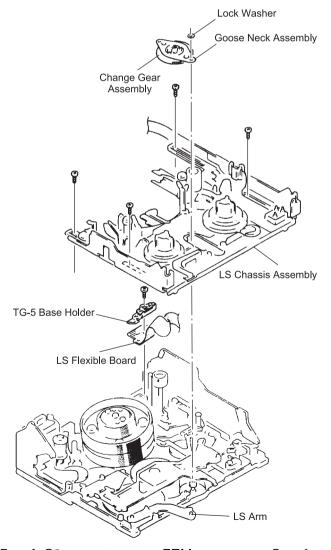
Сборочный чертеж ЛПМ видеокамер Sony (ме-ханизм A)
